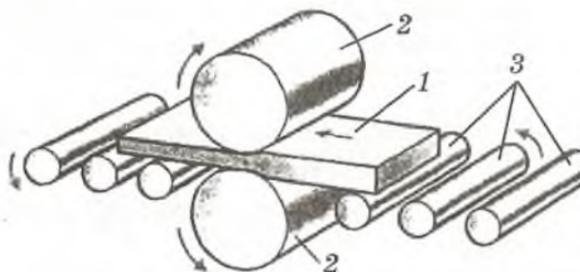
Схема прокатки листового металла: 1 — заготовка из металла, 2 — валки, 3 — ролик
